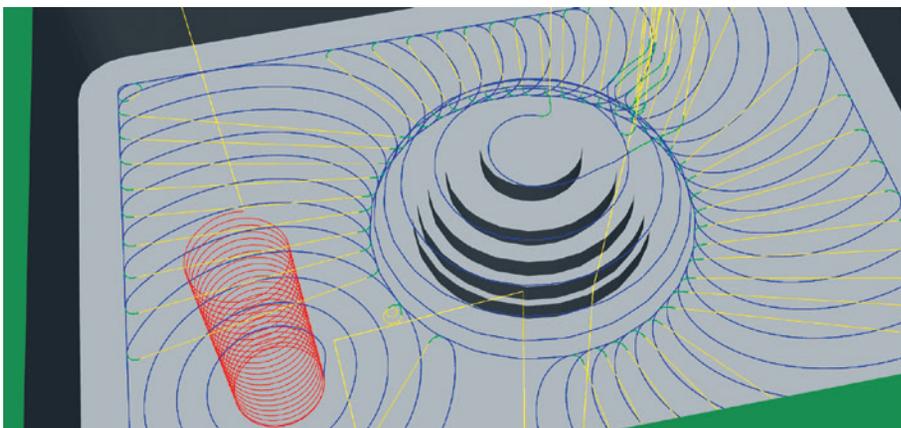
Das Adaptive 3D-Clearing in Fusion 360 entspricht dem Wirbelfräsen.
